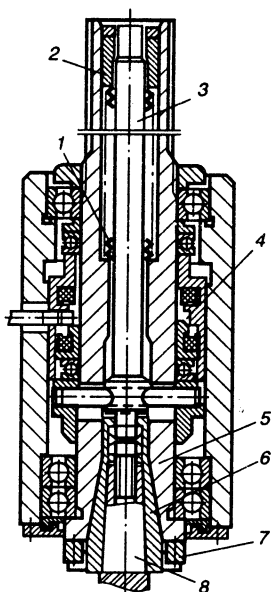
Механизированный зажим инструмента в шпинделе фрезерного станка с ЧПУ
